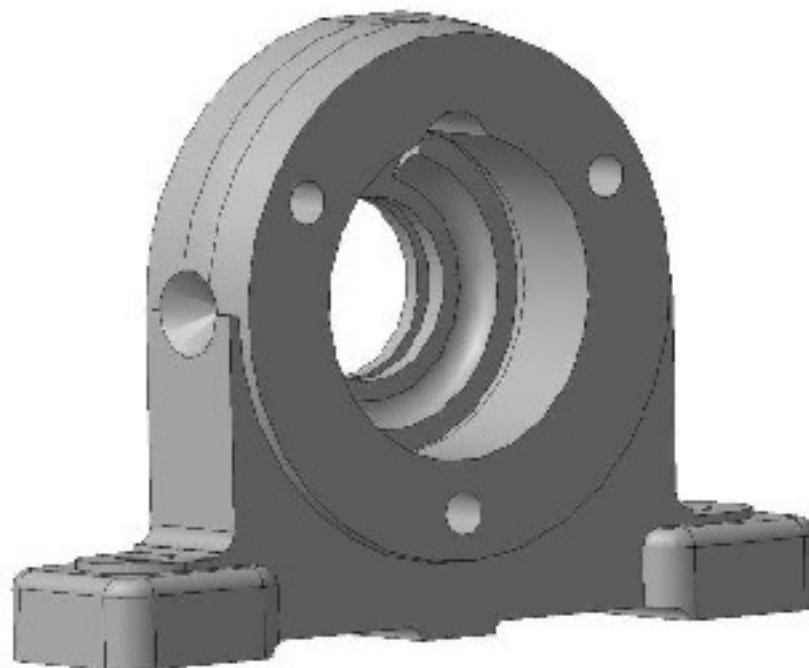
3D-модель деталі «Корпус підшипника 420.008-01»
